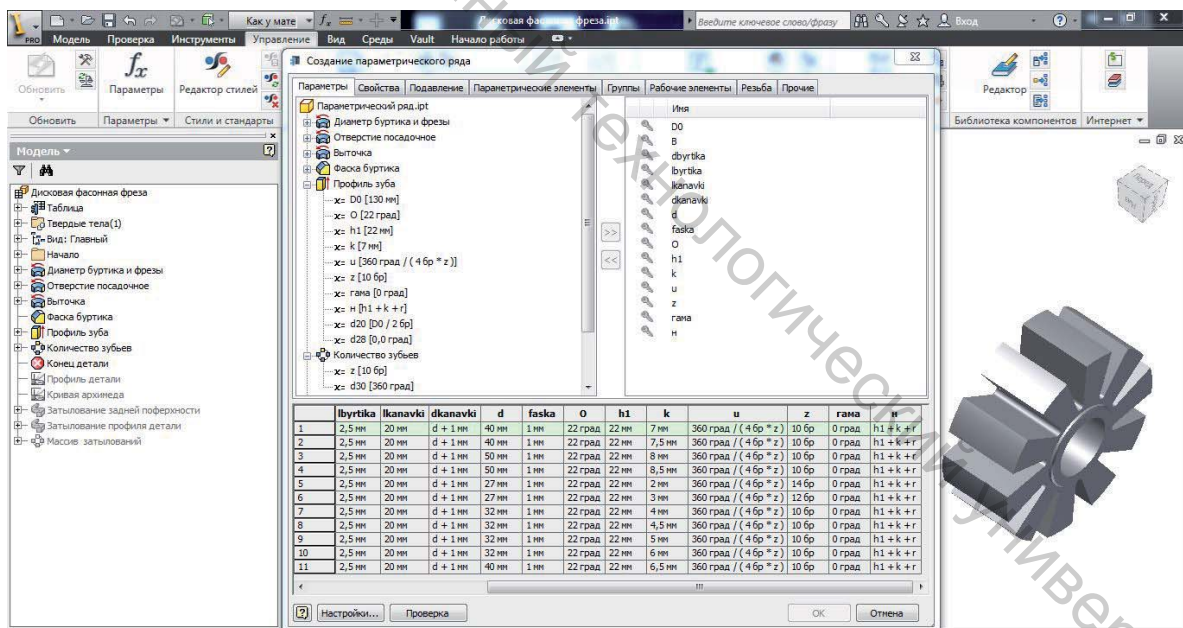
Профиль зуба дисковой фасонной фрезы
